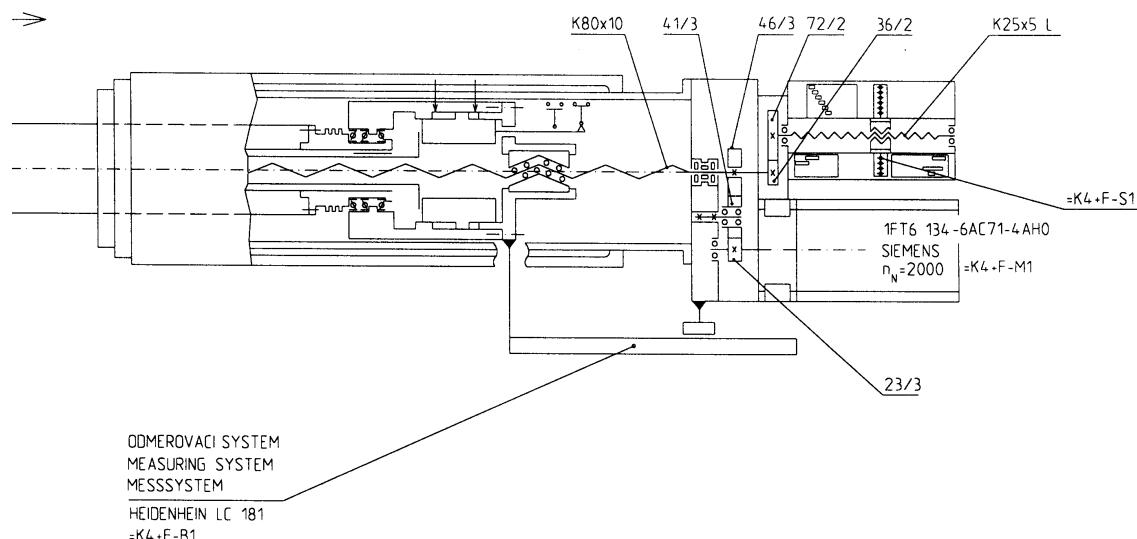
Schéma hlavního pohoru horizontky [ŠMT Plzeň]
